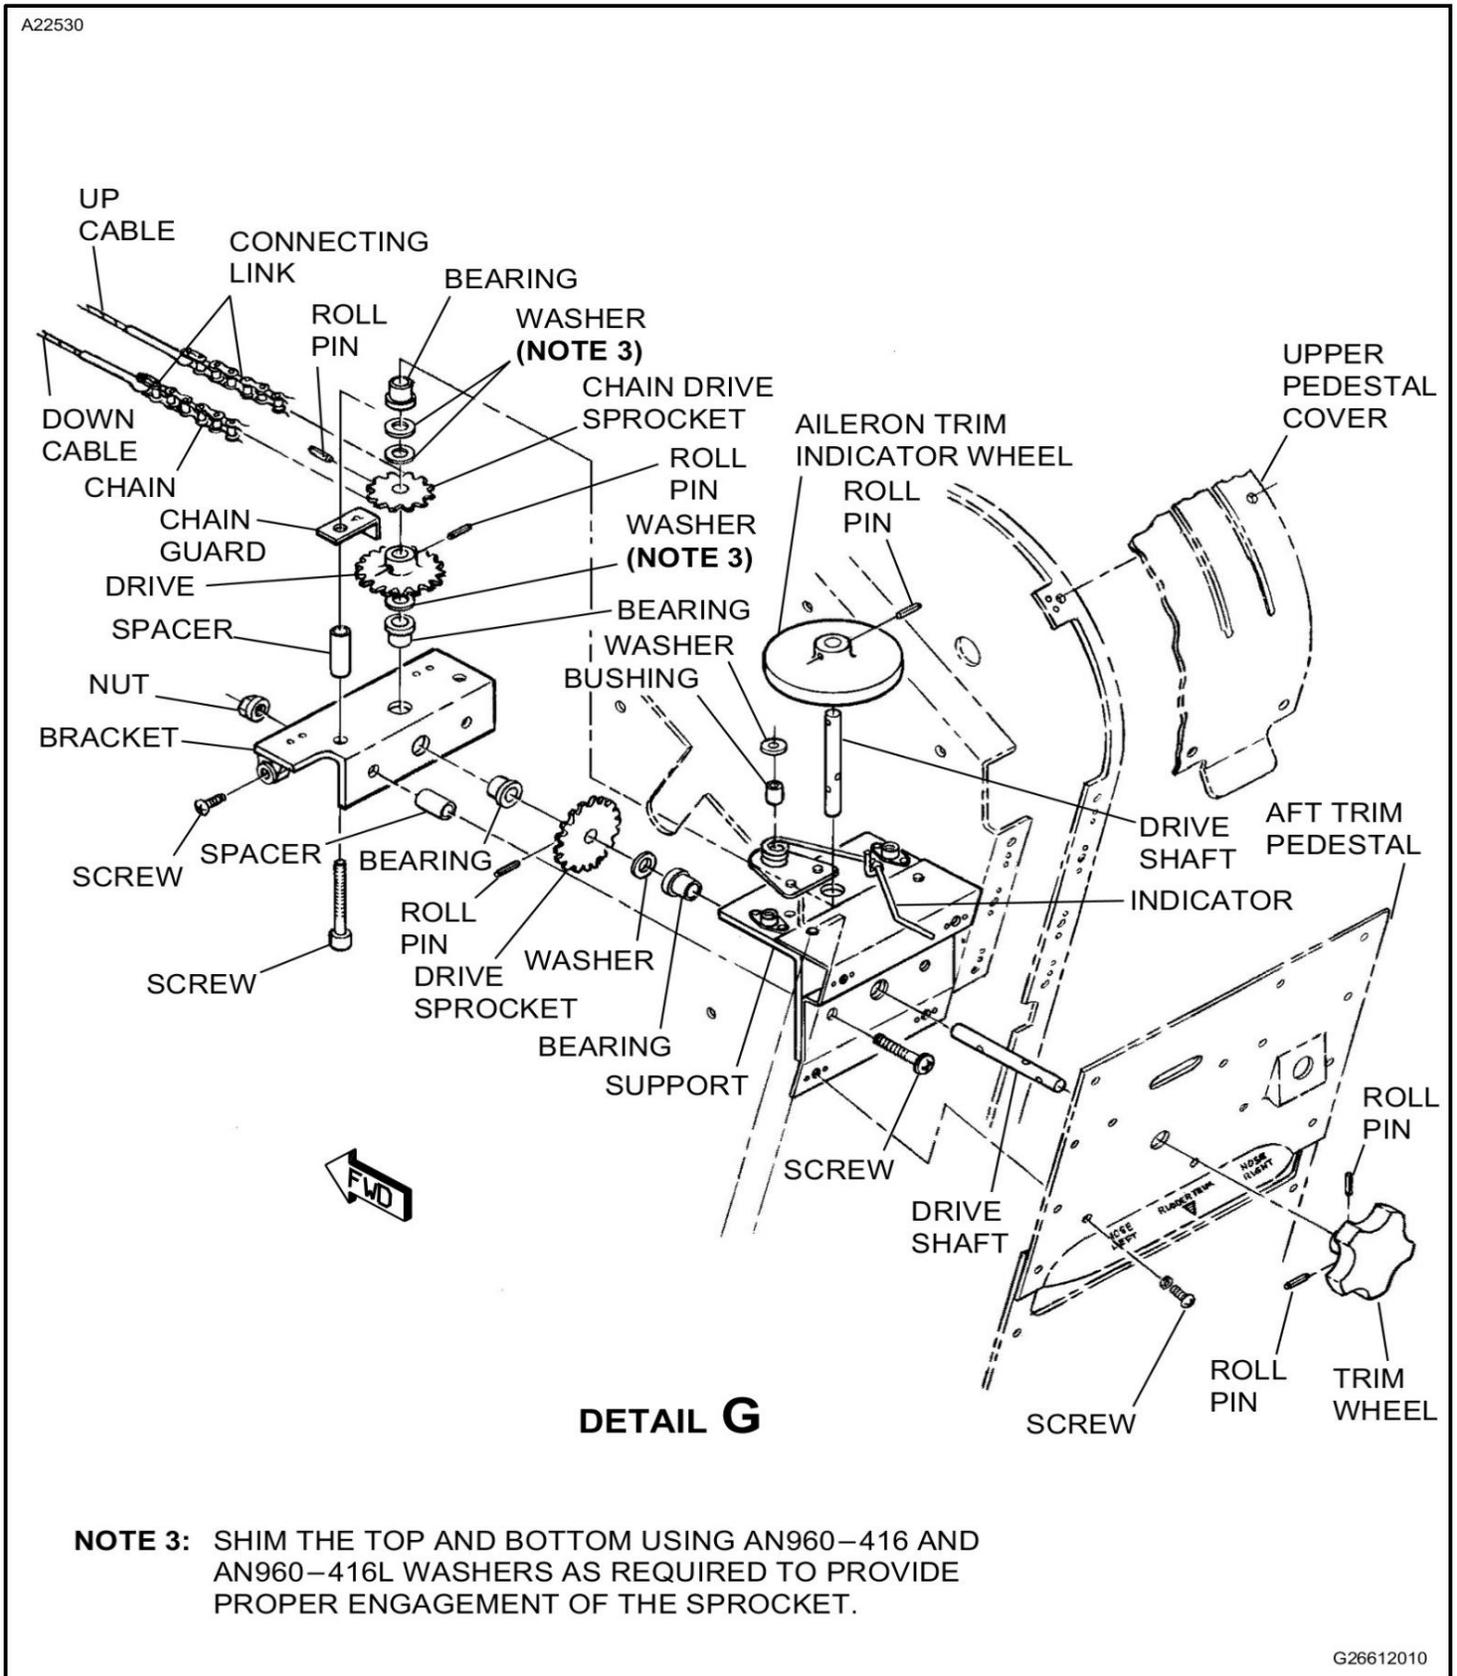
Folha 1: Desmontagem/montagem do atuador do compensador do aileron
